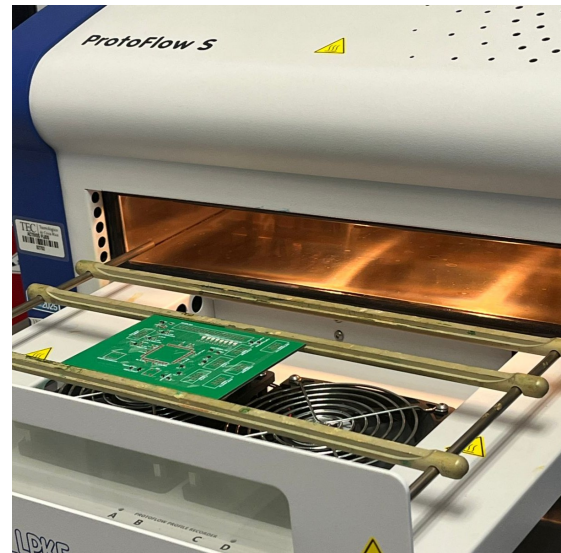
Horneado de la placa para fijar la soldadura de los componentes de montaje superficial.
